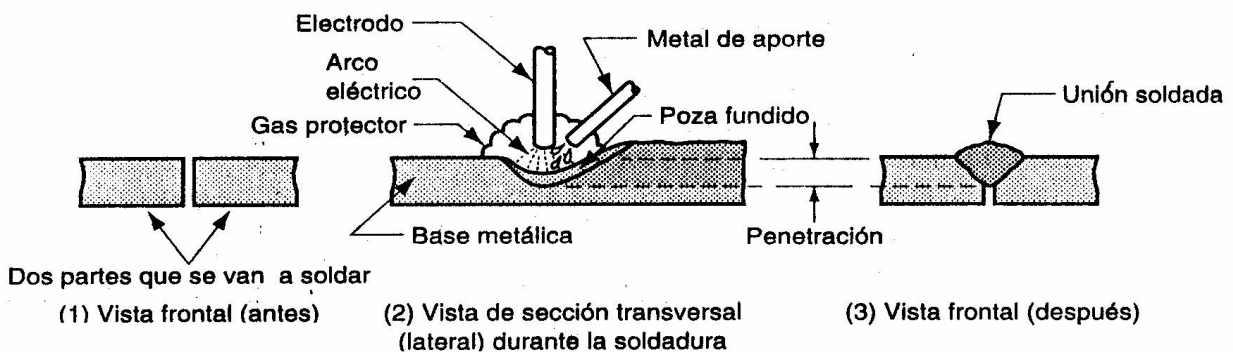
Fundamentos de la soldadura con arco eléctrico: (1) Antes de la soldadura, (2) Durante la soldadura se funde la base metálica y se agrega el metal de aporte al conjunto fundido y (3) La soldadura terminada. Hay muchas variaciones del proceso de soldadura con arco eléctrico.
